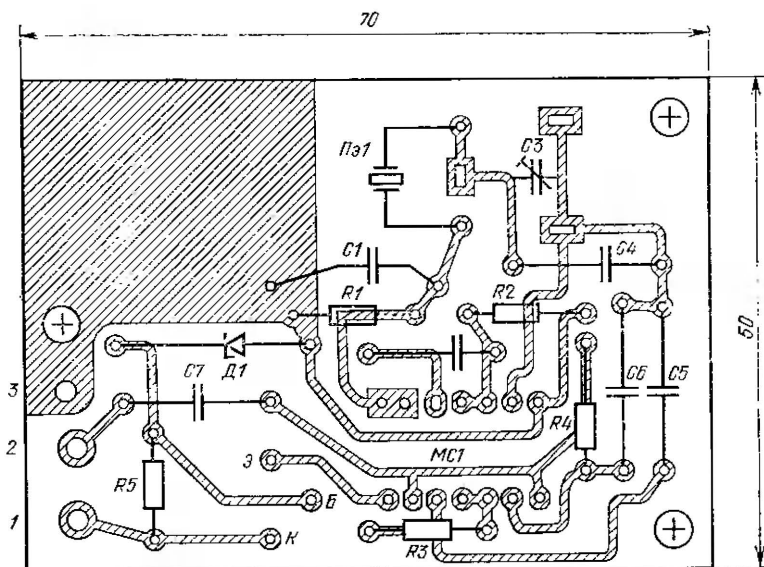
Печатная плата кварцевого калибратора с монтажной схемой (вид снизу)
